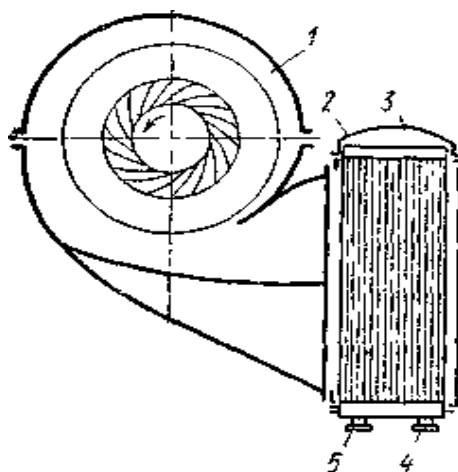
Схема подключения промежуточного холодильника к нижней части корпуса компрессора
